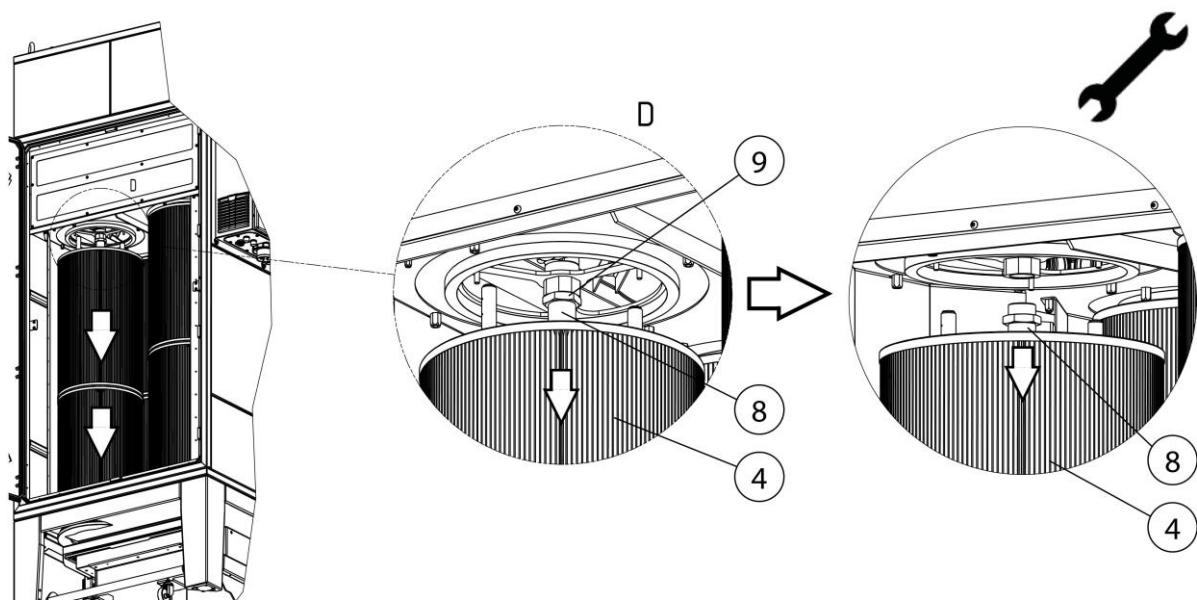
Remplacement du filtre - démontage de la buse rotative
